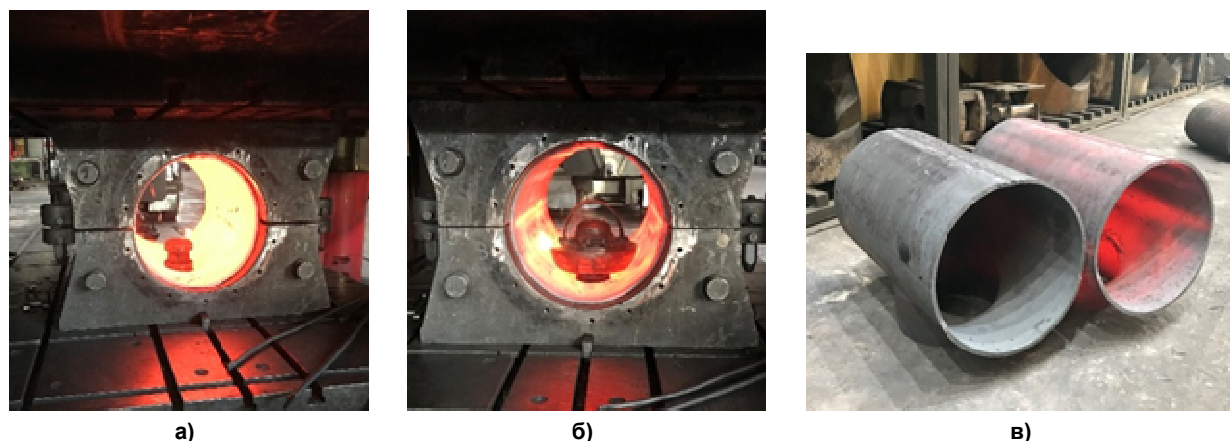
Операция отбортовки: а – обжатие заготовки; б – отбортовка ответвления; в – отбортованные детали
